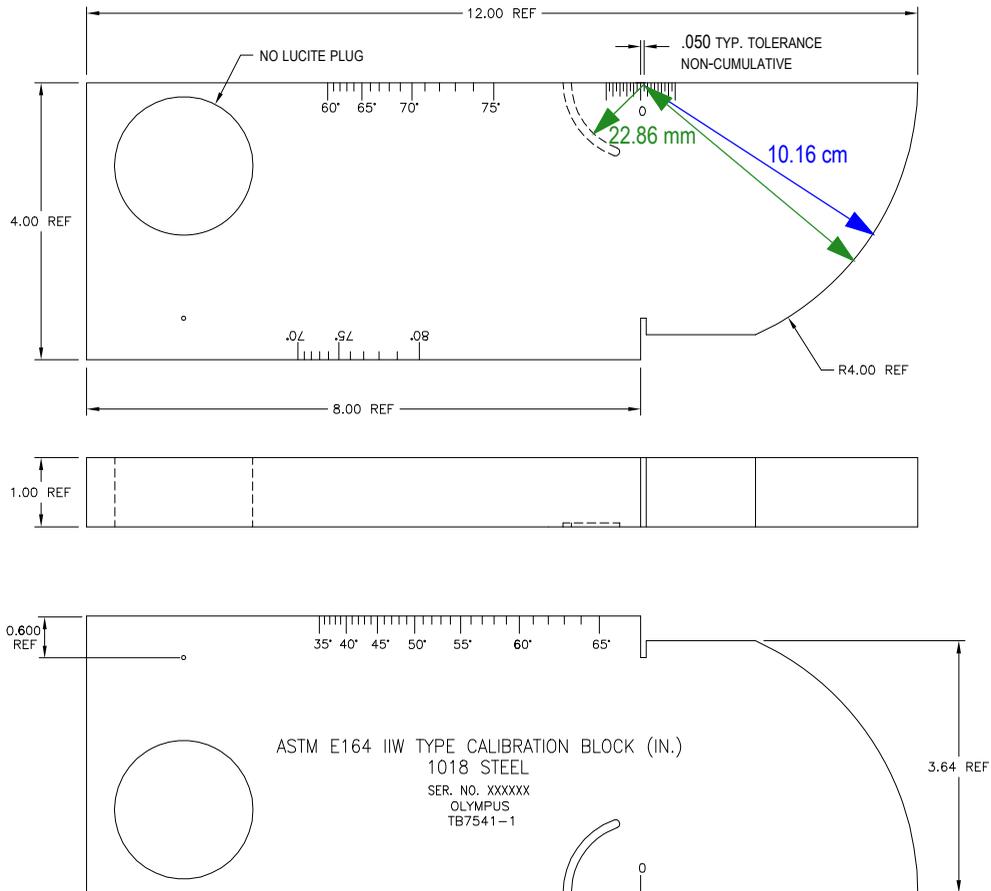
Калибровочный образец ASTM E164 IIW (Арт.: TB7541-1)
